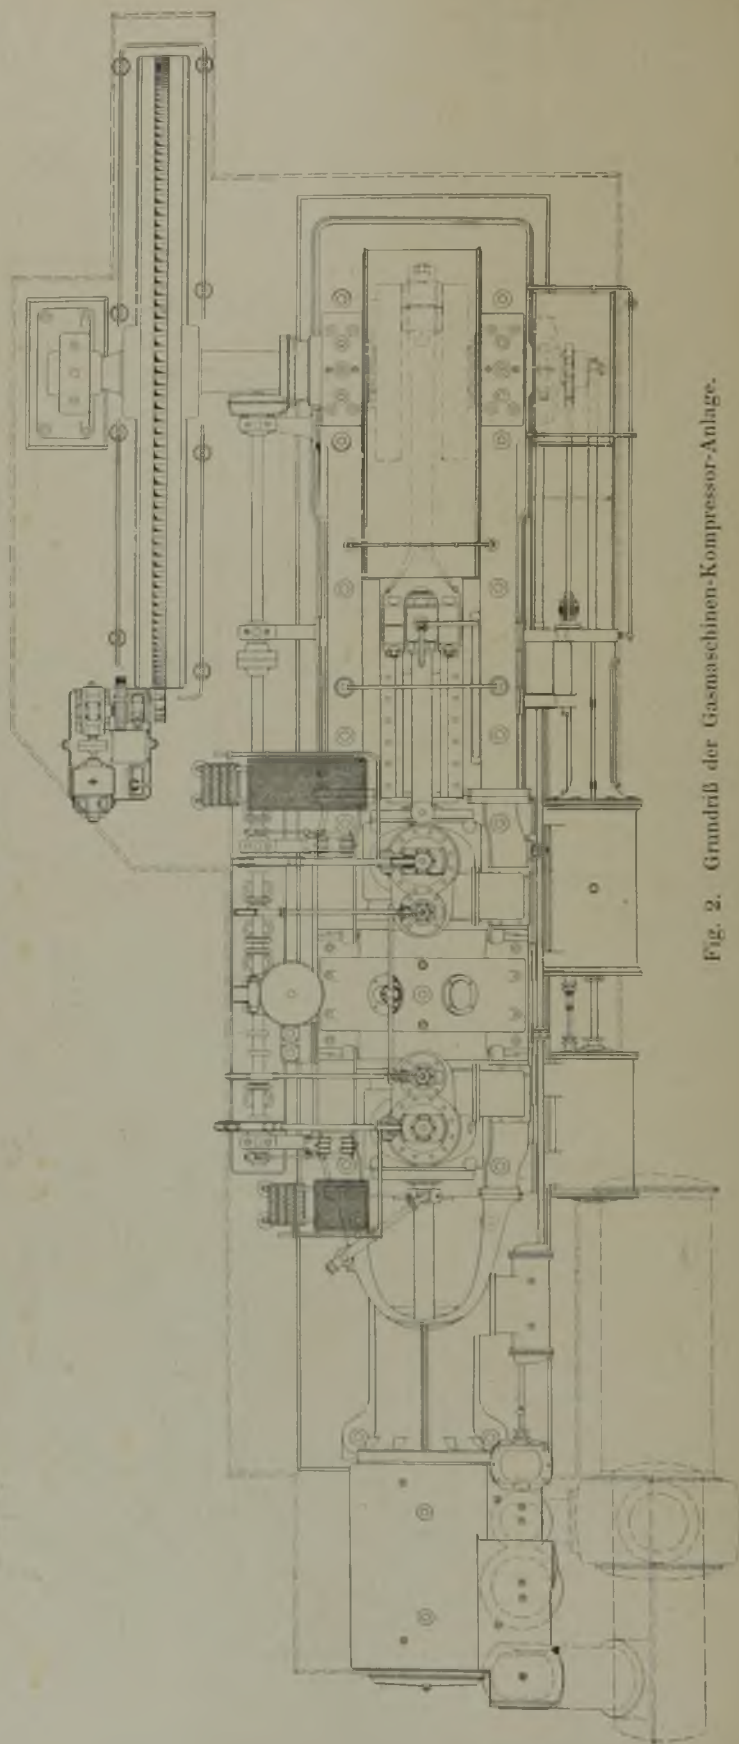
Grundriß der Gasmaschinen-Kompressor-Anlage.
